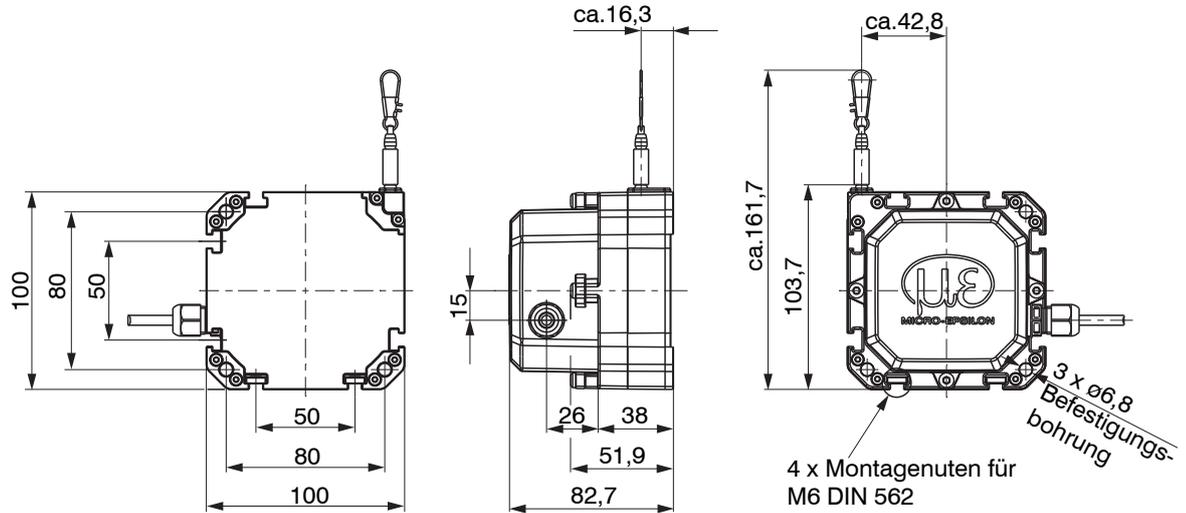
Maßzeichnung WPS-1500-K100, WPS-2500-K100 mit integriertem Kabel, radial, Länge 1 m, Abmessungen in mm
